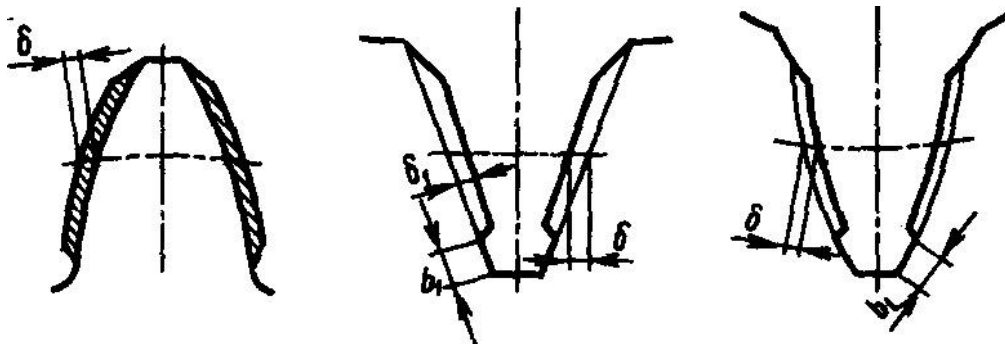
Форма припуска зубьев колес под шевингование и инструмент для их обработки
